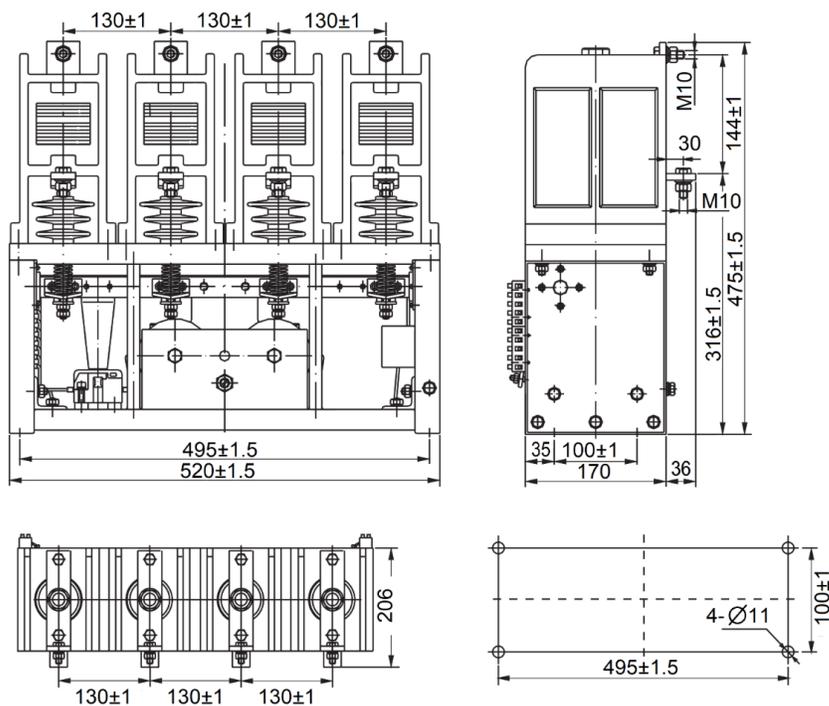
Габаритные размеры контакторов КВТ-6 на номинальные токи 160, 250, 400, 630 А четырёх полюсного исполнения и размеры монтажной площадки.
